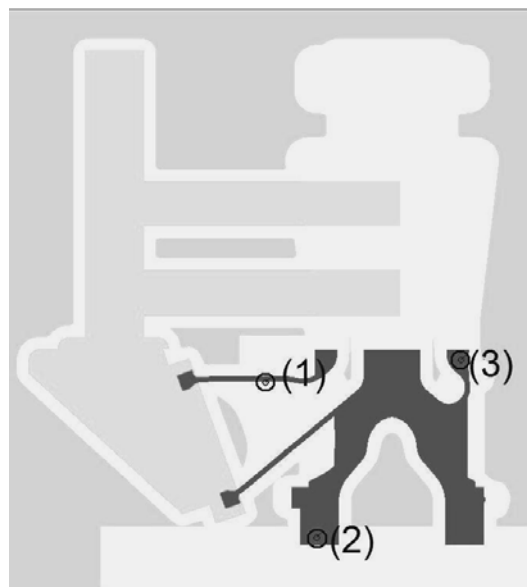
Схема расположения виртуальных термопар на сечении отливки «корпус»:
